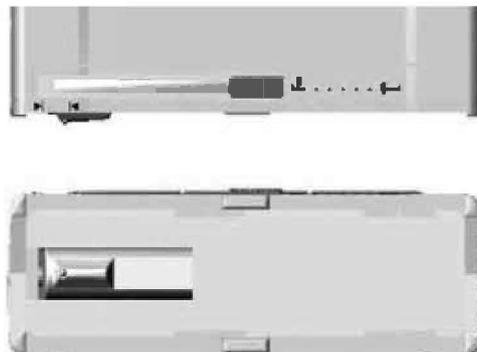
Geöffneter Sensorschacht mit sichtbarem Sensor
